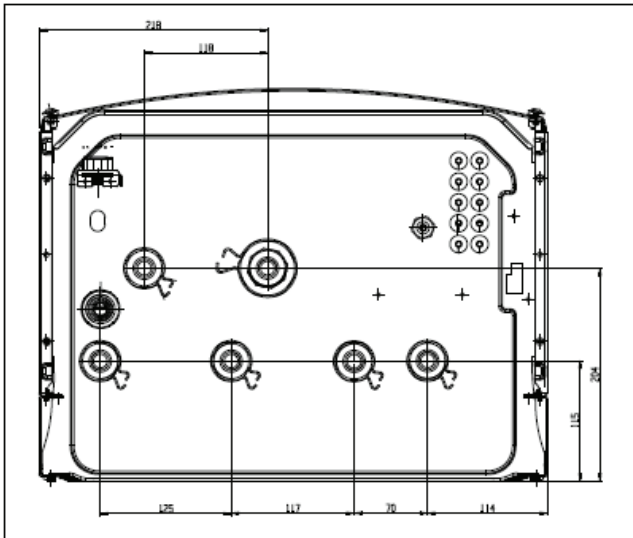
Внутренний настенный блок WPL ... AR-B, габаритные размеры в мм (вид снизу)
